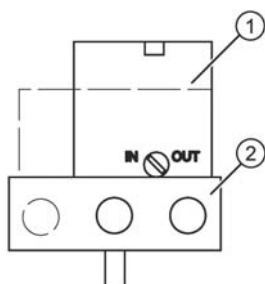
Переключатель воздуха продувки на пневматическом блоке; вид позиционера со стороны пневматических соединений при открытой крышке
